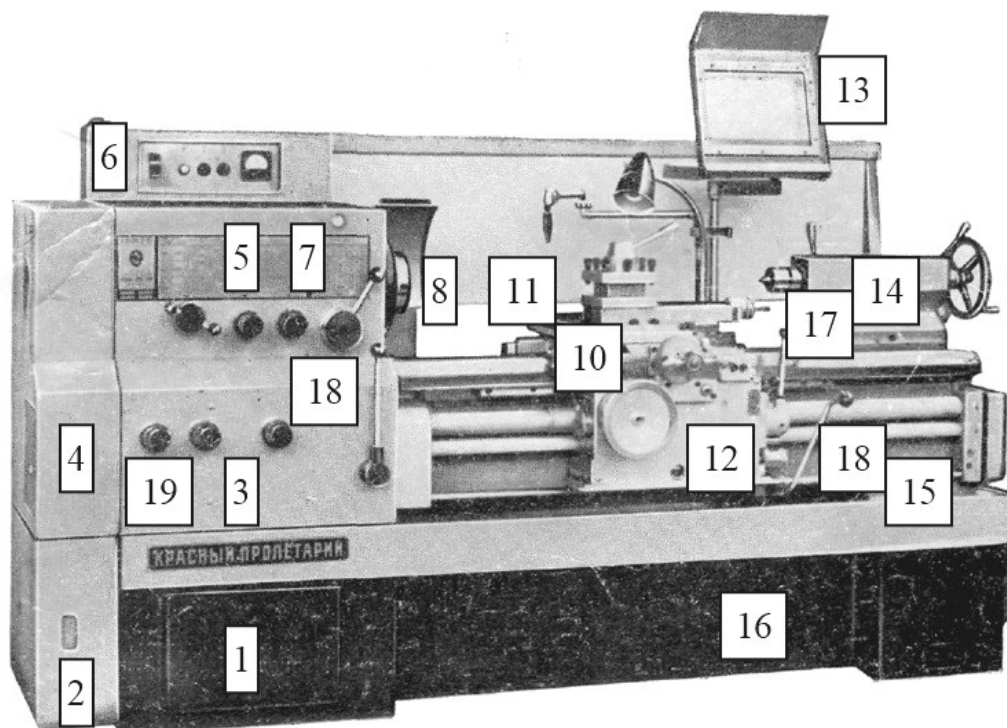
Общий вид станка 16К20: 1 – передняя тумба; 2 – ременная передача; 3 – коробка подач; 4 – гитара сменных колес; 5 – передняя (шпиндельная) бабка; 6 – кнопочная станция; 7 – переключатель перебора; 8 – шпиндель; 9 – люнет; 10 – суппорт; 11 – резцедержатель; 12 – фартук; 13 – предохранительный щиток; 14 – задняя бабка; 15 – станина; 16 – основание; 17 – рукоятка включения перемещения суппорта; 18 – рукоятка включения шпинделя; 19 – рукоятки настройки подачи
